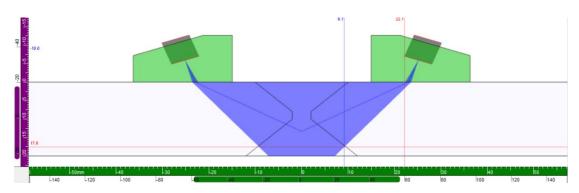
(T=20MM) 双 V 焊缝波束的覆盖范围
